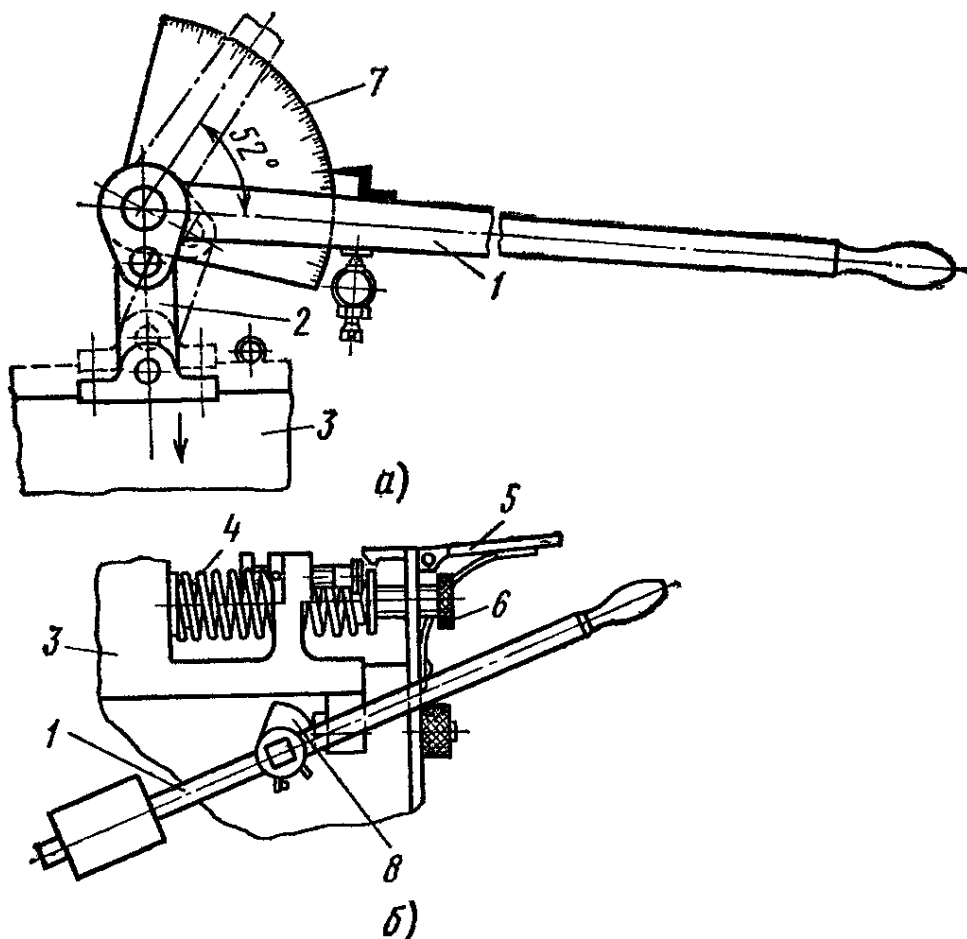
Рычажный (а) и пружинный (б) приводы стыковых машин.
